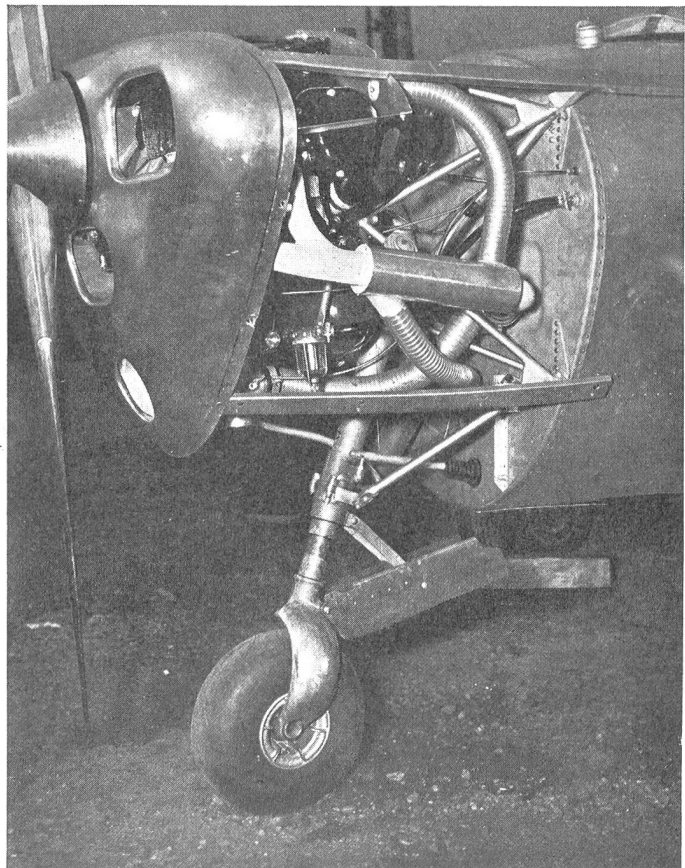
rechts: Rumpfbug des «Ercoupe»-Flugzeugs mit abgenommener Motorverkleidung. Man beachte ganz vorne die verkleidete Propellernabe und die Eintrittsöffnungen für die Kühlluft zur Motorkühlung. Der 75pferdige, luftgekühlte «Continental»-Motor ist ein sogenannter Boxer-Motor, das heißt ein Flugmotor mit gegenüberliegenden Zylindern. Dieser Motor ruht in einem Motorbock aus Stahlrohren mit der sog. Dreipunkt-Aufhängung. – Das wannenartige Gebilde oberhalb des Bugrades enthält den Öldruck-Stoßdämpfer. – Durch die obere Kühlluft-Eintrittsöffnung links oben erblickt man die dünnwandigen Kühlrippen eines Motorzylinders.
